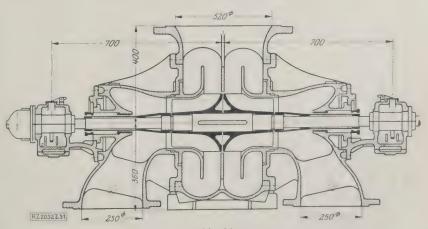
Schraubenpumpe Myria von Weise Söhne mit doppelseitigem Einlauf.
